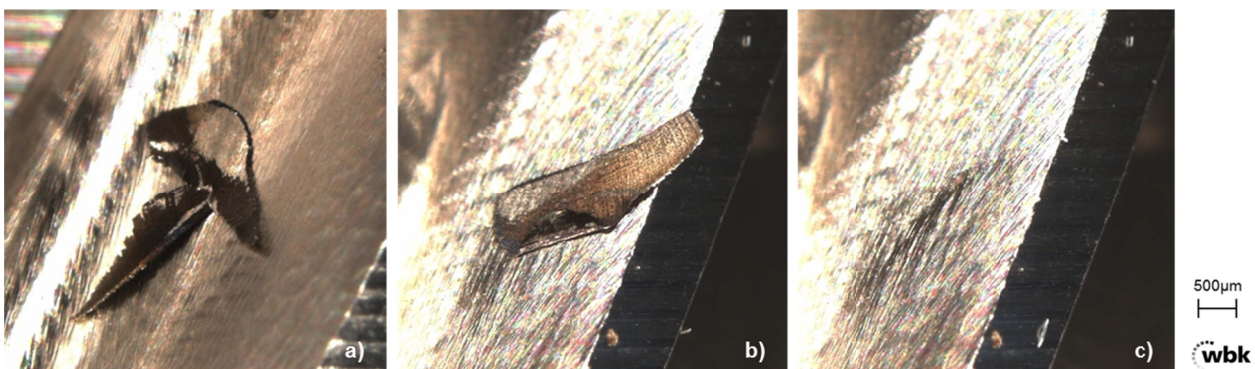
Feste und lösbare Spanklemmer [BEC-06]
